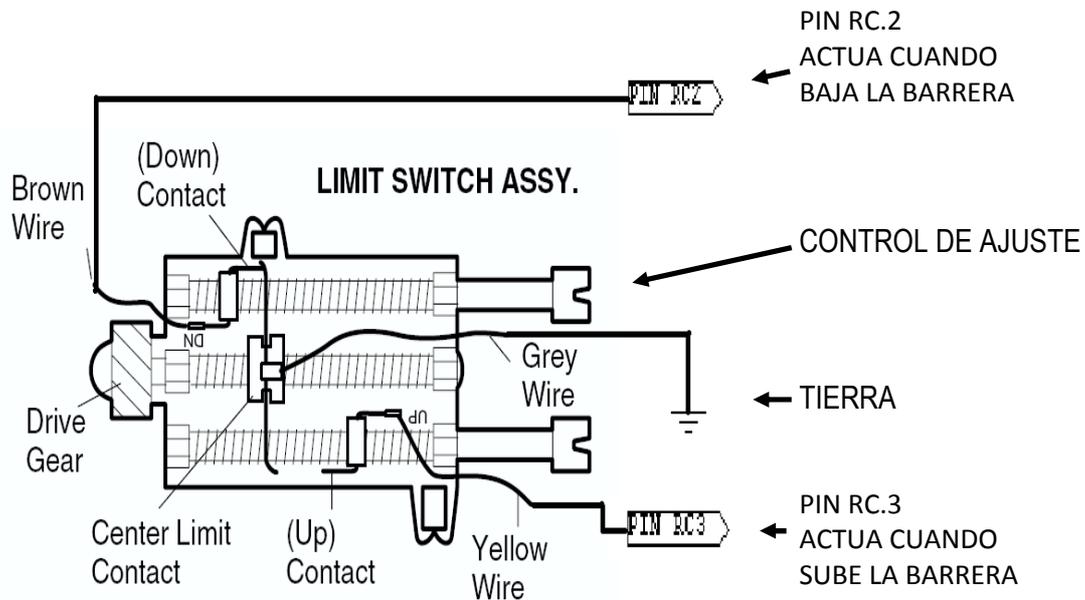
Conjunto de LIMIT SWITCH utilizado
